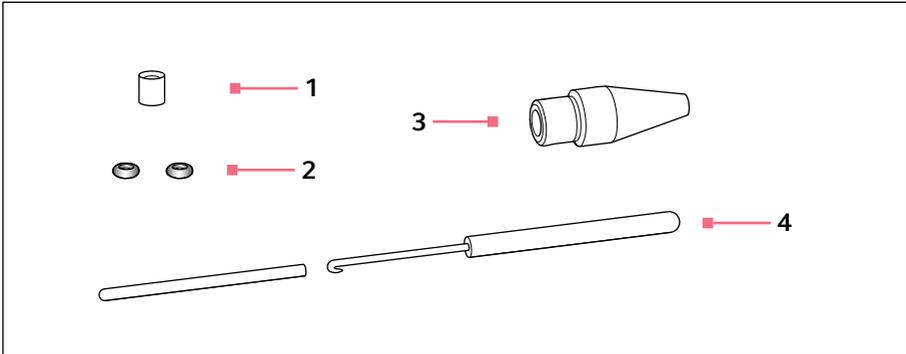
Spannkopf 4 mit Entnahmewerkzeug
